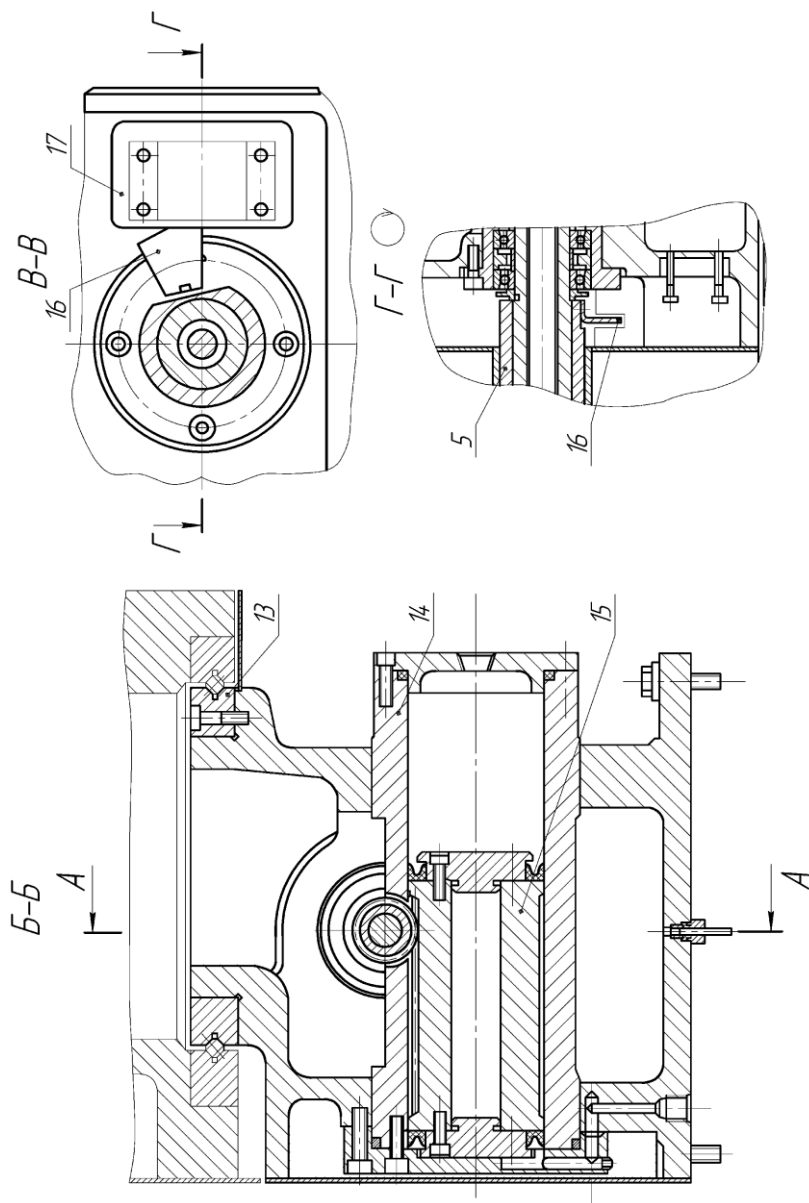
Механизм привода поперечной подачи шлифовальной головки
